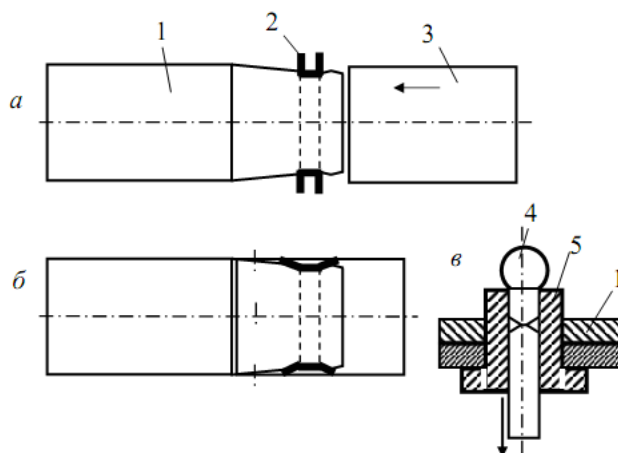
Способ соединения труб по длине: а – подготовка труб для сборки; б – труба после сборки; в – способ установки заклепок
